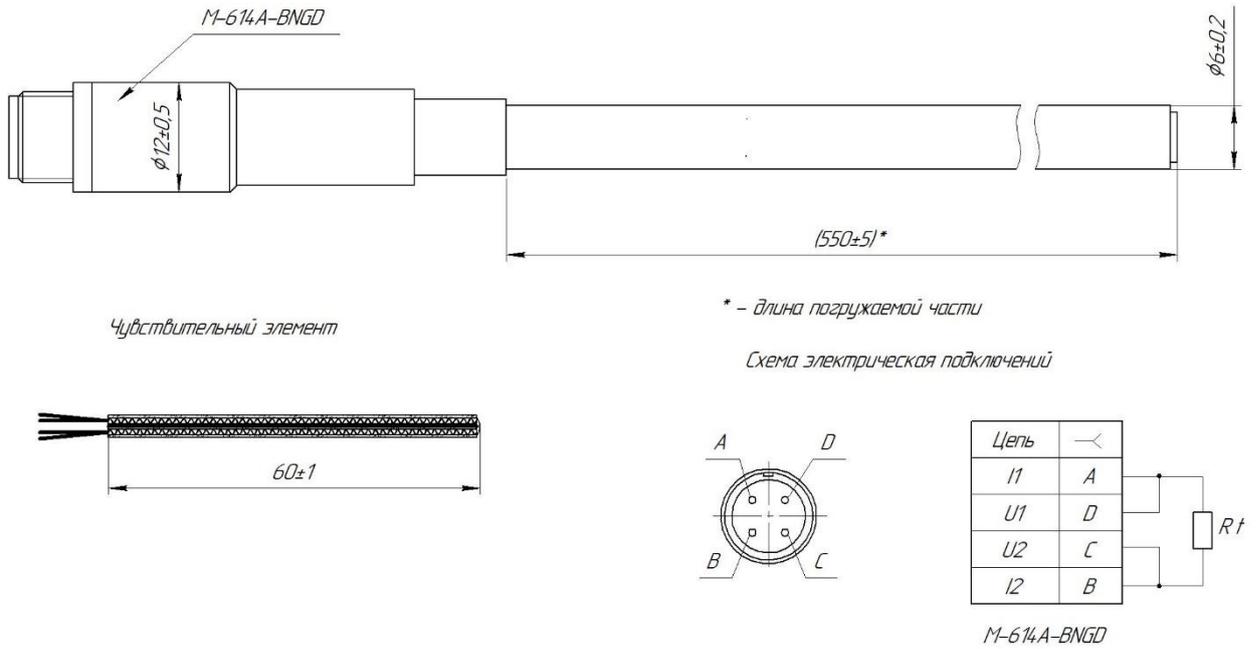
Конструкция и габаритные размеры термометра ЭТС-5М
